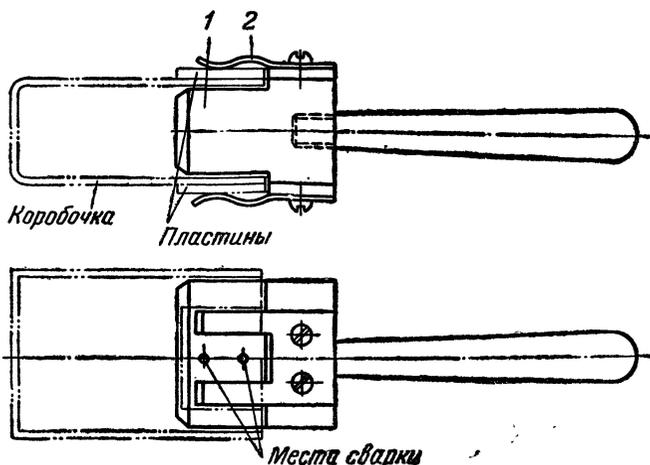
Приспособление для сварки кольцевых швов.
